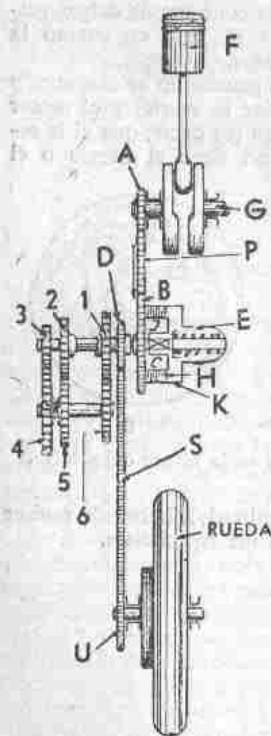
Transmisión desde el motor *F* a la rueda.
